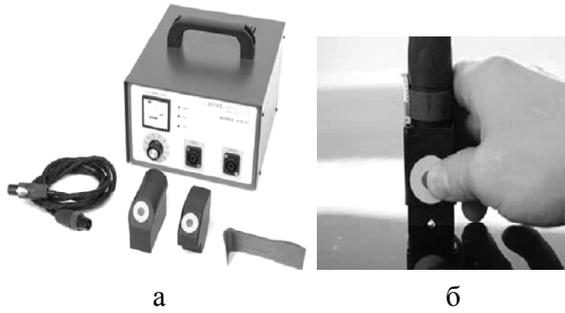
Устройство «Hotbox» для рихтовки кузовных панелей с помощью локального нагрева: а – внешний вид; б – инструмент в действии
